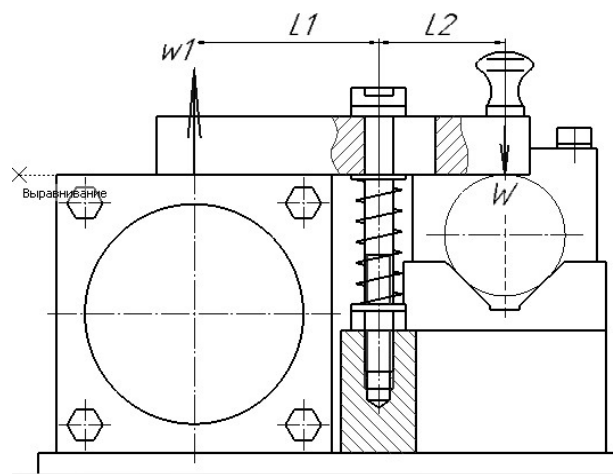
Загальний вигляд приводу пристрою
